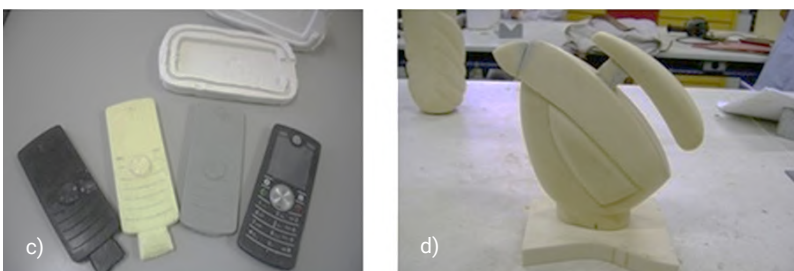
Exemplos (c) e (d) da construção de modelos – oficinas práticas.
